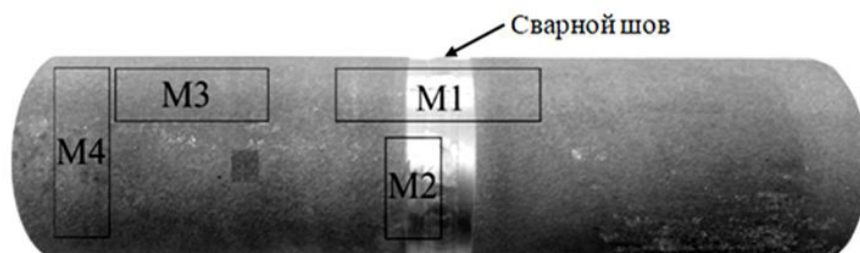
Участки вырезки образцов из трубного сварного соединения для металлографического анализа и измерения микротвердости сплава
